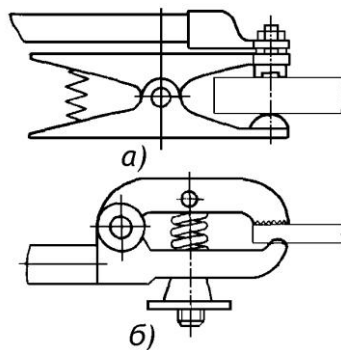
Зажимы для присоединения сварочного провода к изделию, где а – пружинный, б – винтовой
